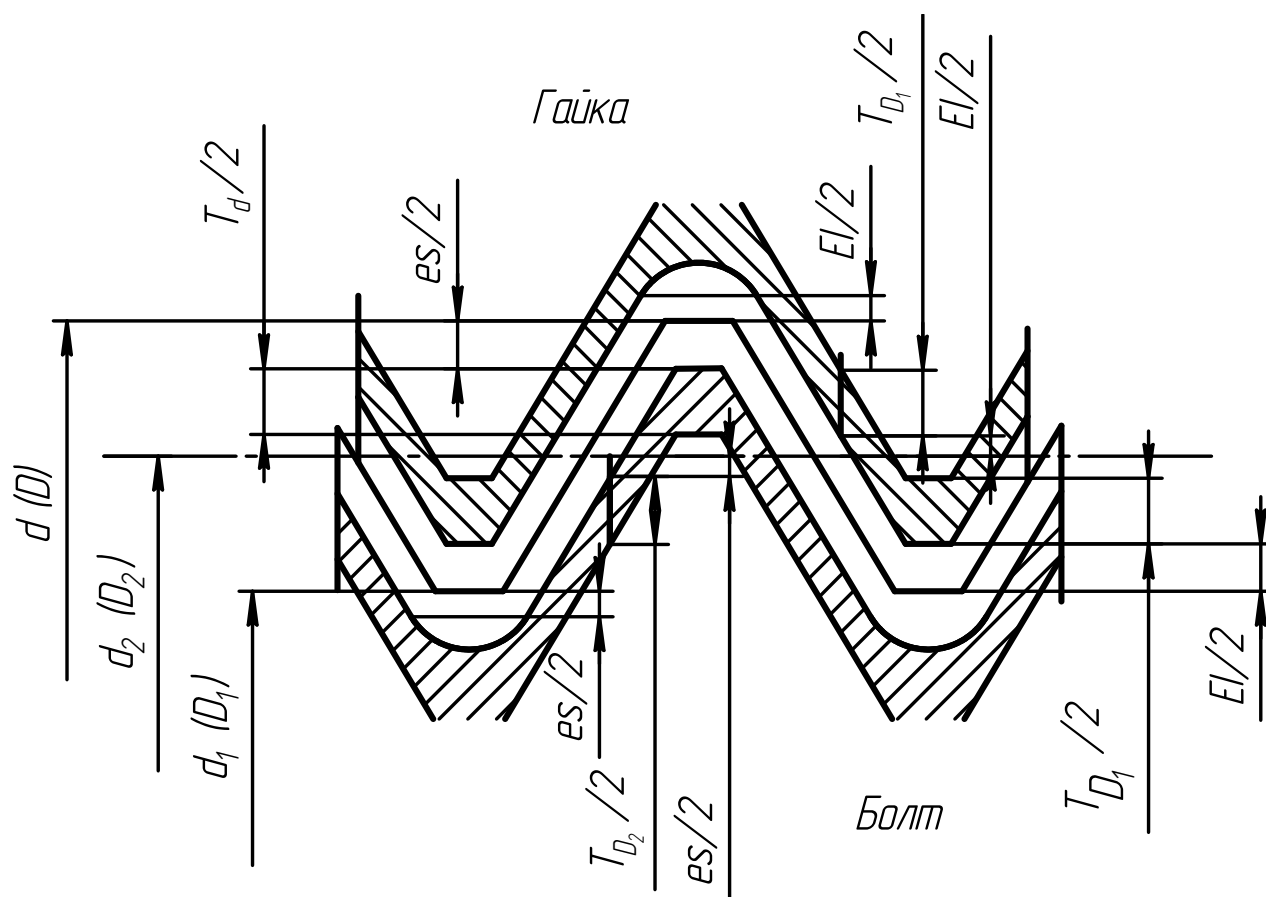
Расположение полей допусков метрической резьбы болта и гайки при посадке с зазором
